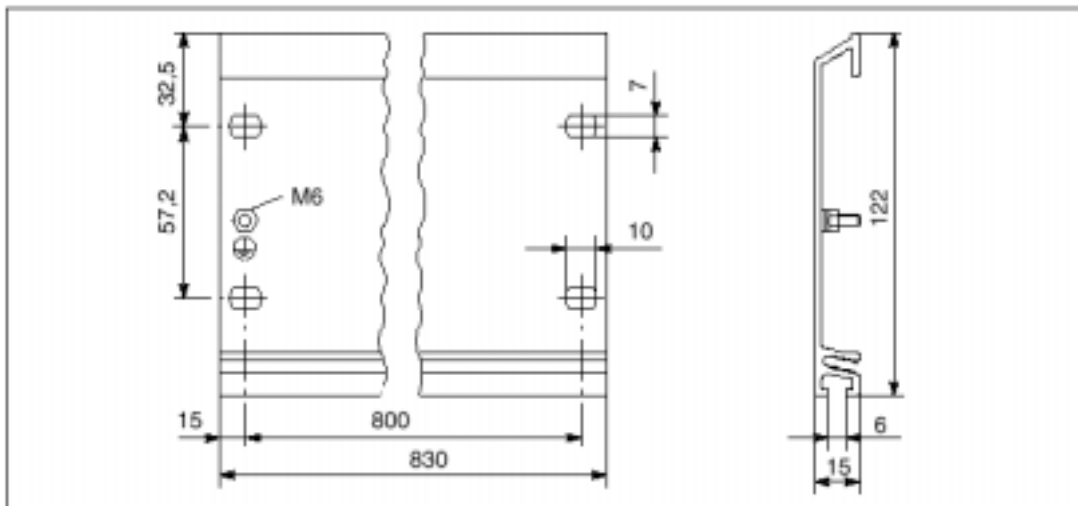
Чертеж с размерами профильной шины стандартной ширины 830 мм
